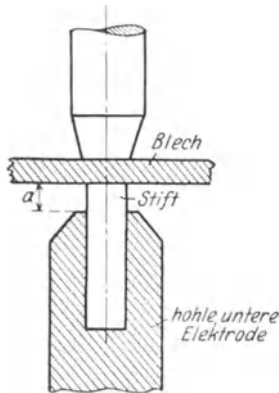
Elektroden für Stiftanschweißung.
